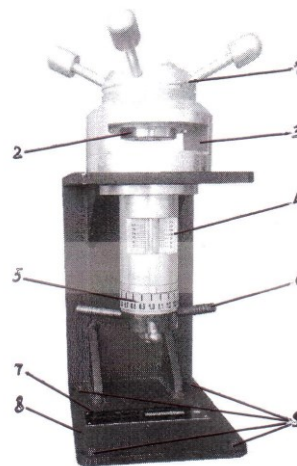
Штамп Еріксена NOVOTEST SHE-1: 1 – поворотний притискний пристрій; 2 – матриця; 3 – проріз для зразків; 4 – пристрій розрахунку глибини вдавлювання пуансона (вертикальна шкала); 5 – пристрій розрахунку глибини вдавлювання пуансона (кругова шкала); 6 – кермо; 7 – маркування; 8 – станина; 9 – отвори для фіксування приладу
